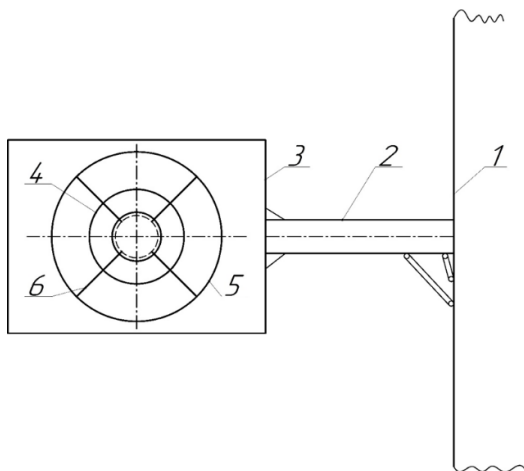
Схема распределительного оборудования для реализации симметричного способа подачи ПГМ на диск: 1 - базовое шасси; 2 – манипуляторное оборудование; 3 – бункер; 4 – лоток; 5 – диск; 6 – лопатка диска
